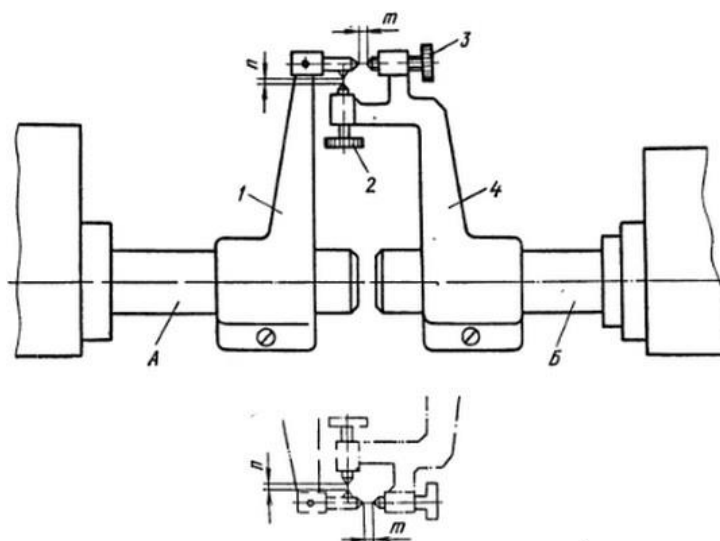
Схема проверки соосности валов с помощью специального поворотного приспособления
